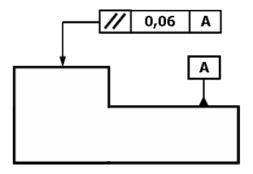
Indicação de tolerância de paralelismo em desenho técnico
